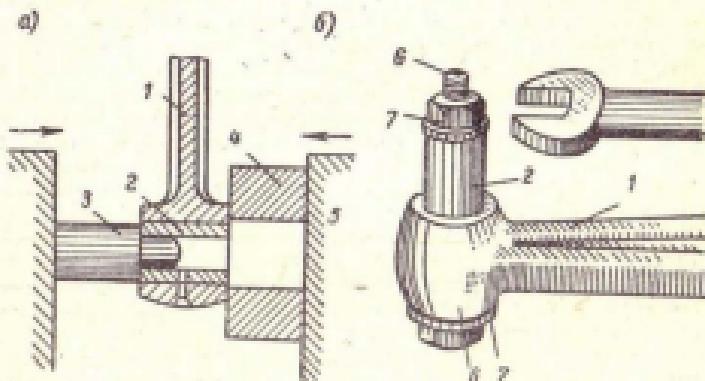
Выпрессовка и запрессовка втулки верхней головки шатуна с помощью:
